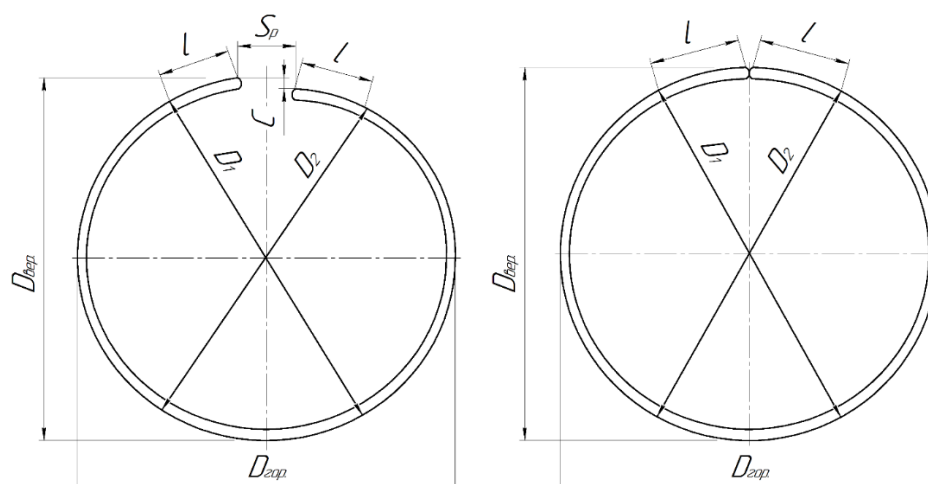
Схема измерения геометрии заготовки после шаговой формовки и сборки
